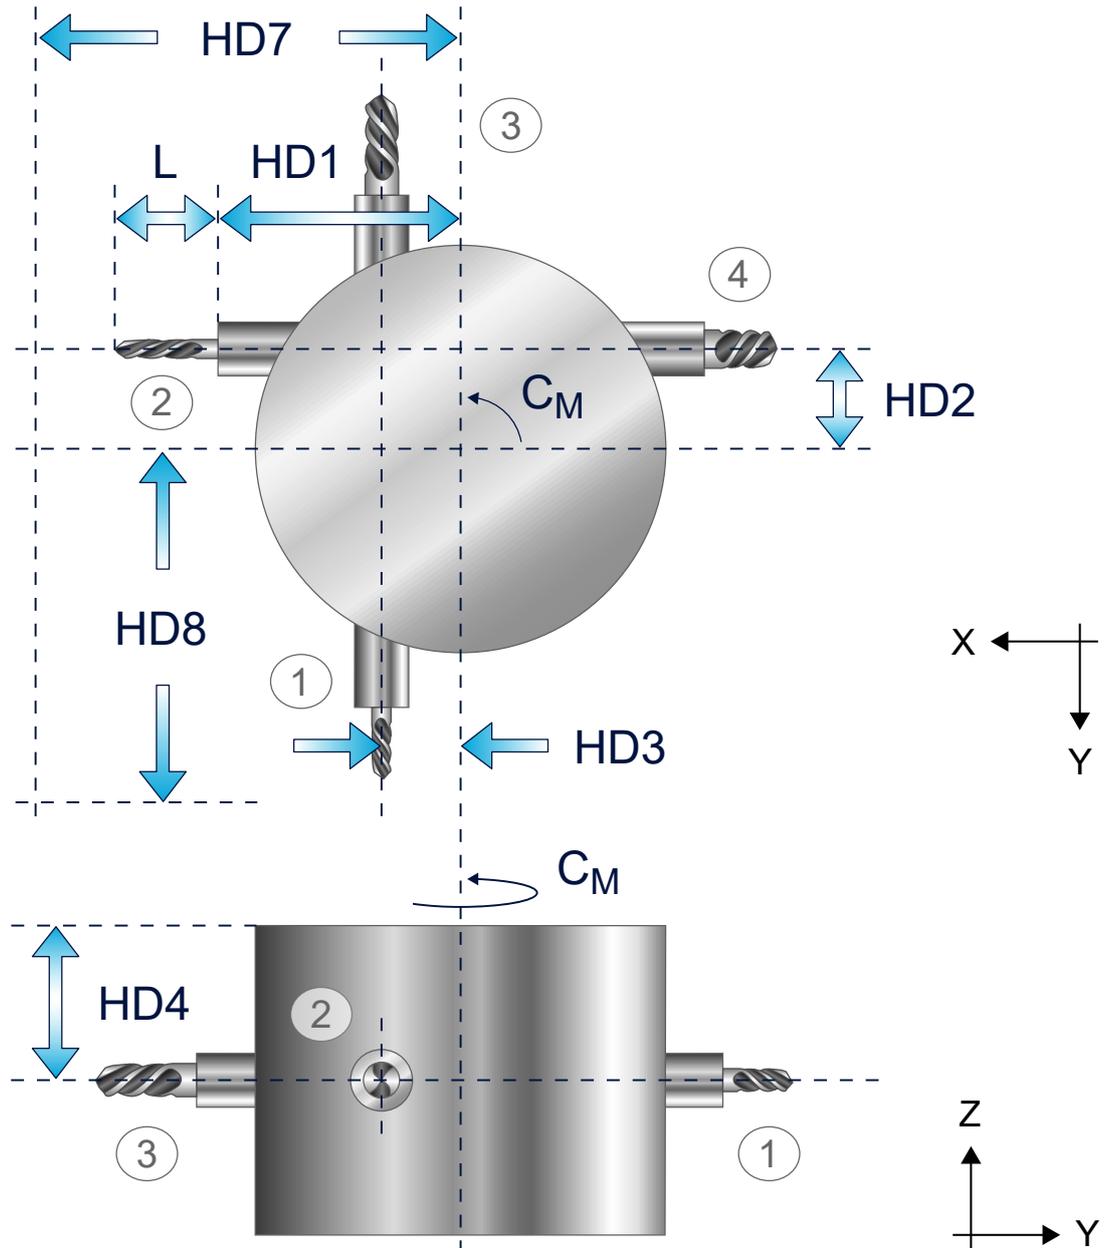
4-achsige Kinematik mit Kreuzkopf für 4 Werkzeuge
